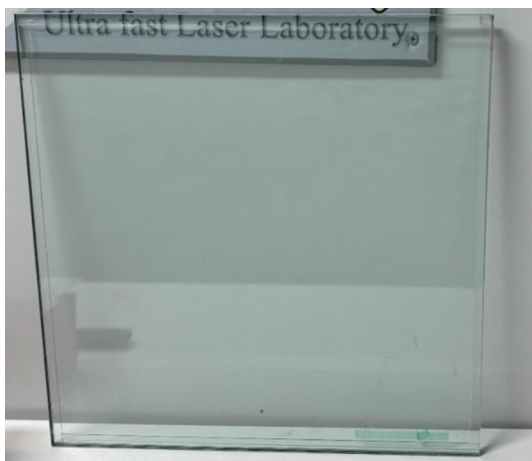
焊接后的全钢化真空玻璃实物图(40 cm×40 cm)
